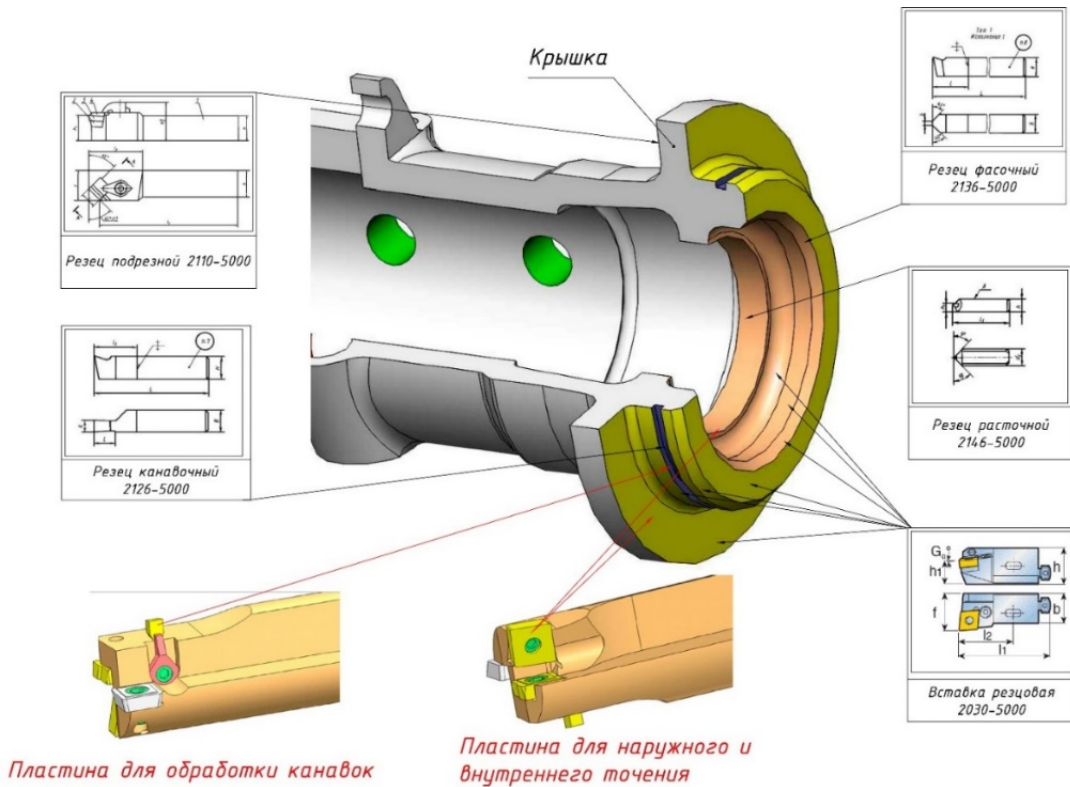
Обработка цилиндрических и торцевых поверхностей
